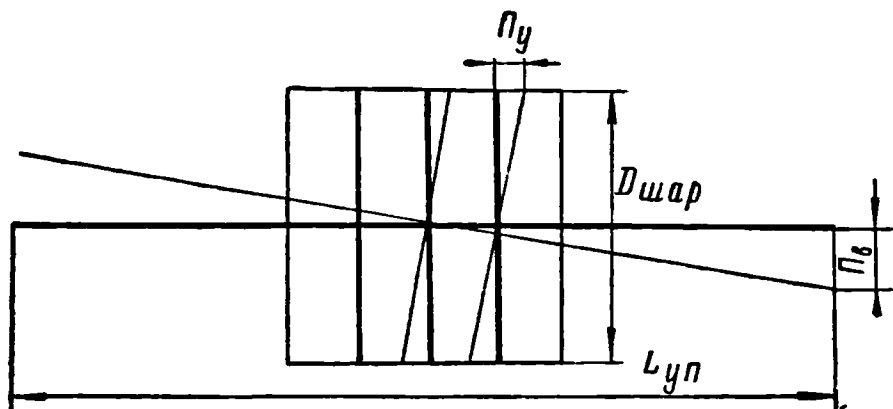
Схема возникновения перекоса упорного вала относительно корпуса упорного подшипника при его сборке.
